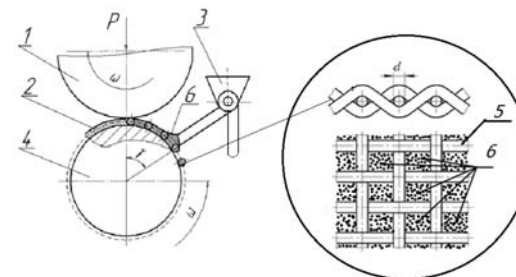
Схема приварки металлического порошка: 1 – роликовый электрод, 2 – приваренный слой, 3 – бункер, 4 – деталь, 5 – сетка, 6 – порошок, d – диаметр проволоки сетки
